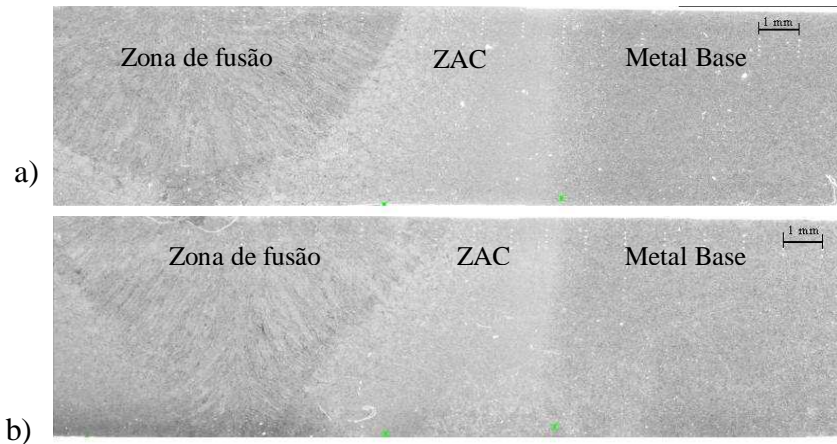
Macrografías de las uniones soldadas, a) como soldada, b) con tratamiento de alivio de tensión
